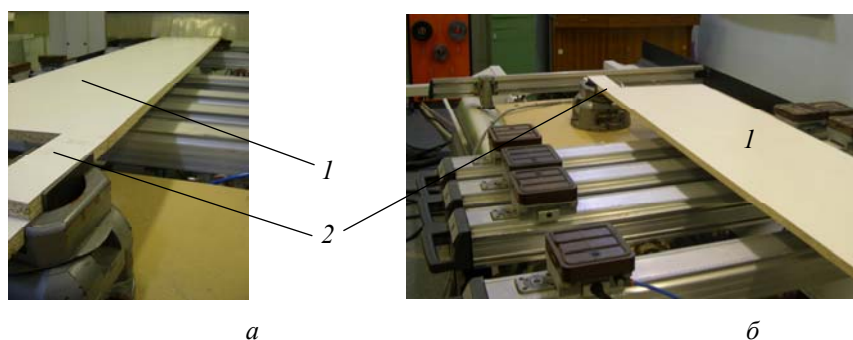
Схема крепления заготовок на рабочих столах станка при проведении экспериментов:
